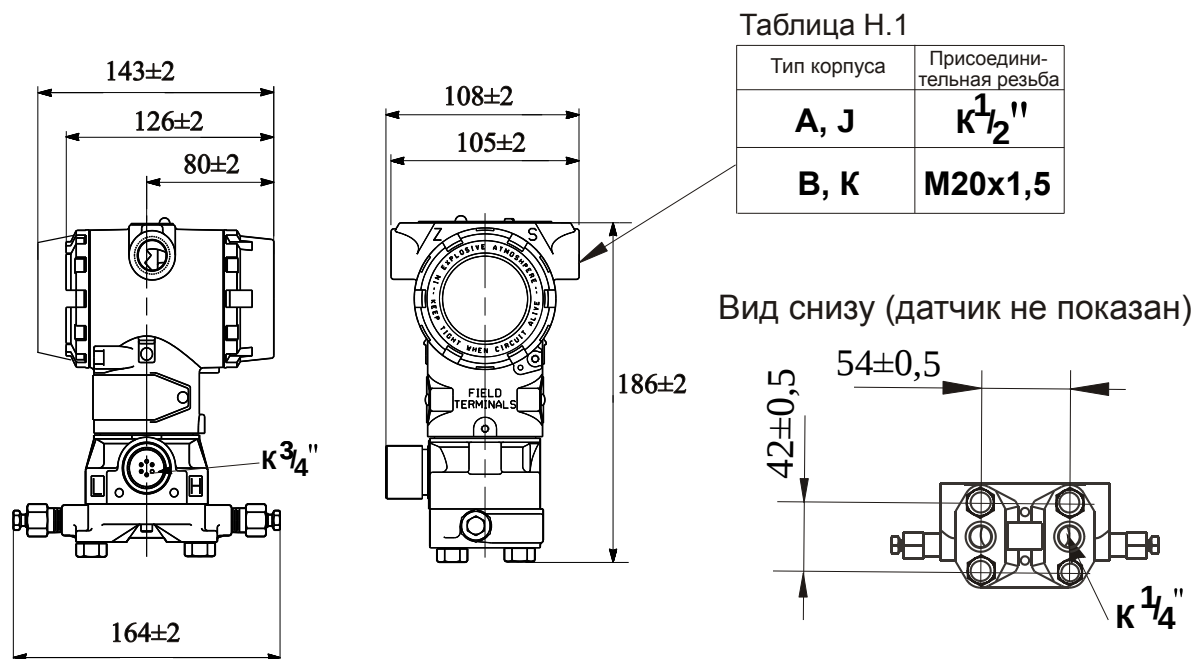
Габаритные и присоединительные размеры датчика давления 3095FB (корпус PlantWeb®) с фланцем Coplanar®
